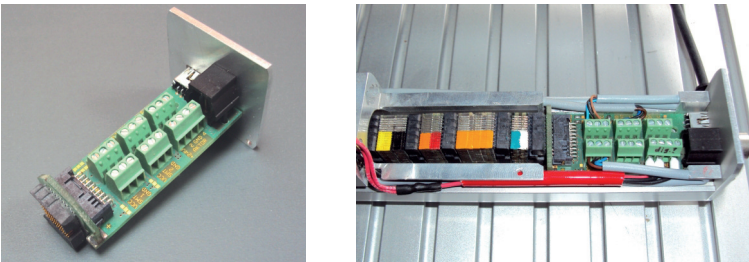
Lösung 2 des Anschlussinterface: links Grundaufbau, rechts Aufbau mit Baueinstapel
